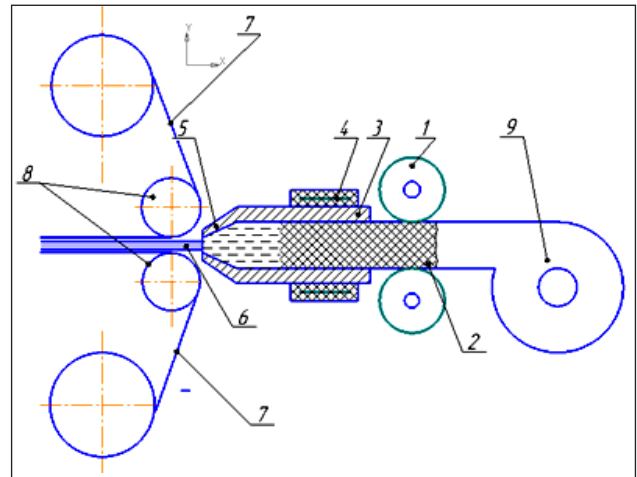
Схема зварювання розплавленим прутком: 1 – подавальний механізм; 2 – полімерний пруток; 3 – канал для плавлення полімерного прутка; 4 – нагрівальний блок; 5 – сопло; 6 – розплав полімеру; 7 – рулони пакувального матеріалу; 8 – притискні ролики; 9 – бухта
